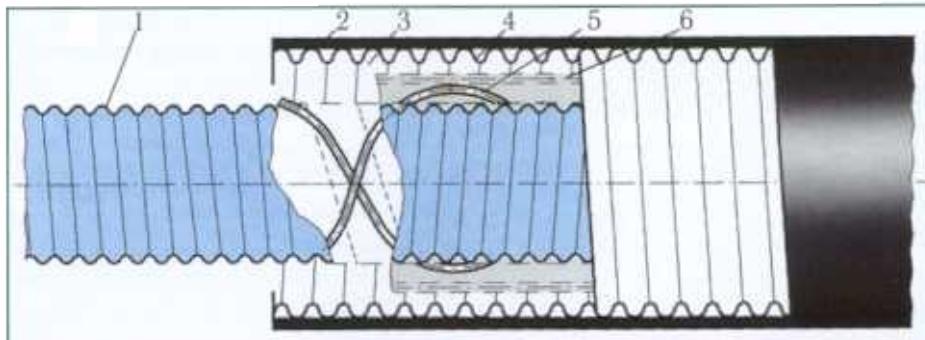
Разрез криогенного трубопровода «Криофлекс»: 1, 4 — спиральные сварные трубопроводы (внутренний и внешний) из нержавеющей стали; 2 — защитная наружная цилиндрическая оболочка из полизтилена; 3 — вакуумное пространство; 5 — спиральная изолирующая прокладка; 6 — многослойная экранно-вакуумная теплоизоляция из полизиэтилентерефталатной пленки (ПЭТ), металлизированной с двух сторон алюминием.
